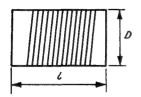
Ansicht einer Zylinderspule mit Maßbezeichnungen
